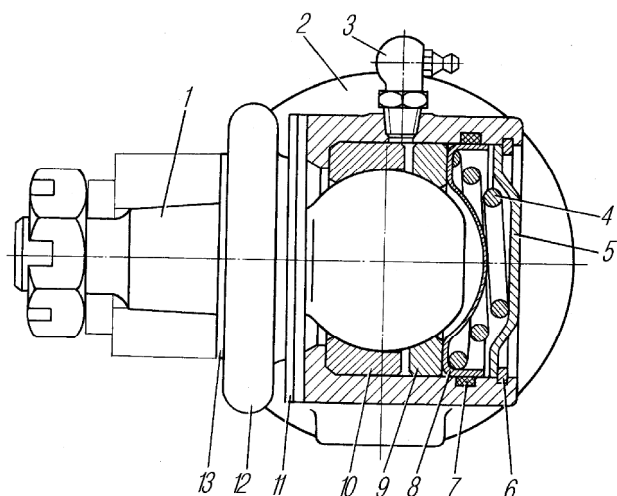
Шарнир рулевого привода: 1- палец шаровой; 2- наконечник; 3- масленка; 4- пружина; 5- заглушка; 6- кольцо стопорное; 7- кольцо уплотнительное; 8- обойма пружины; 9- вкладыш нижний; 10- вкладыш верхний; 11- накладка; 12- муфта защитная; 13- шайба
